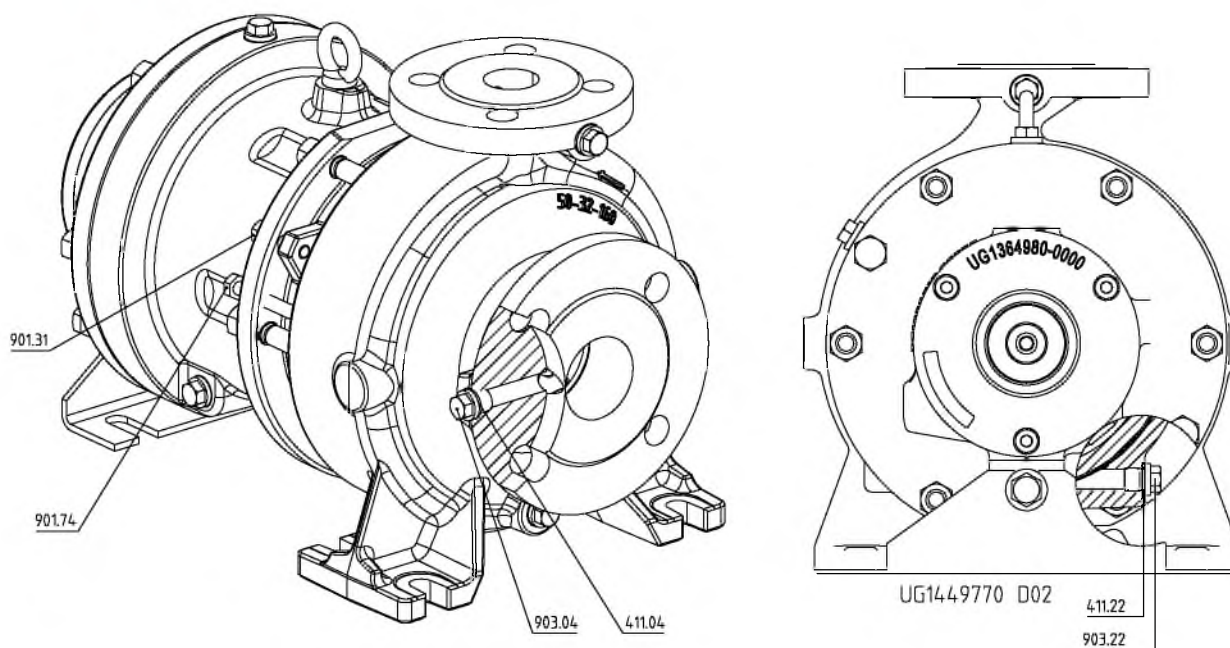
Крепление крышки корпуса с напорной стороны на корпусе насоса для исполнения с зажимной крышкой
